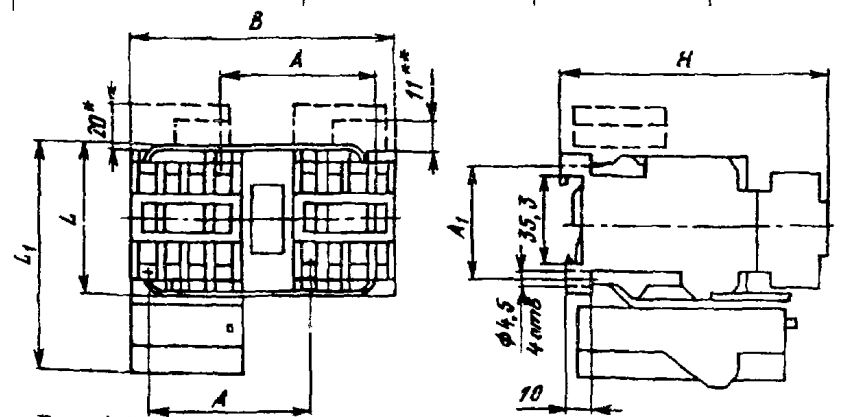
Габаритные и установочные размеры пускателя реверсивного ПМ12-010 степени защиты IP00 и IP20
